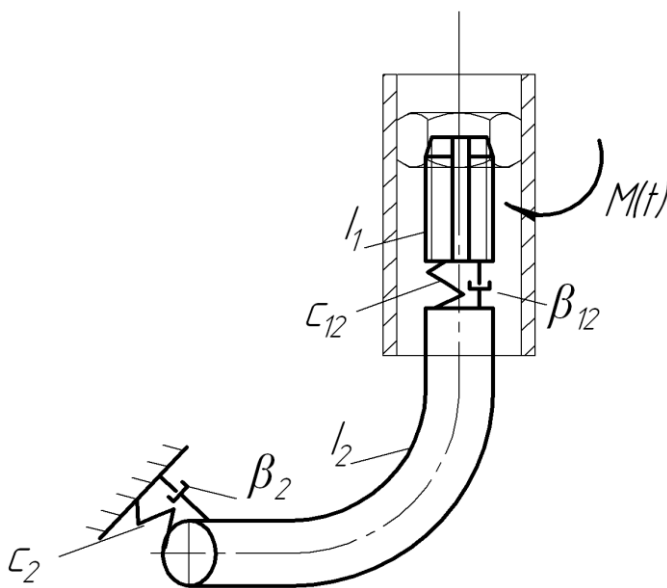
Розрахункова схема частини пристрою для наризання рiзби в гайках
